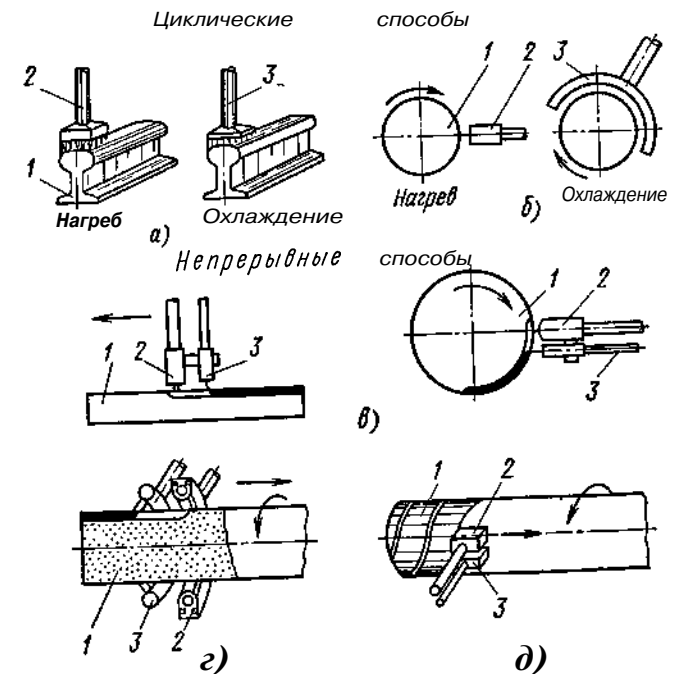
Способы пламенной поверхностной закалки: а — стационарный; б — быстрого вращения; в — непрерывно-последовательный; г — комбинированный кольцевой; д — комбинированный спиральный; 1 — изделие; 2 — горелка; 3 — разбрызгиватель
